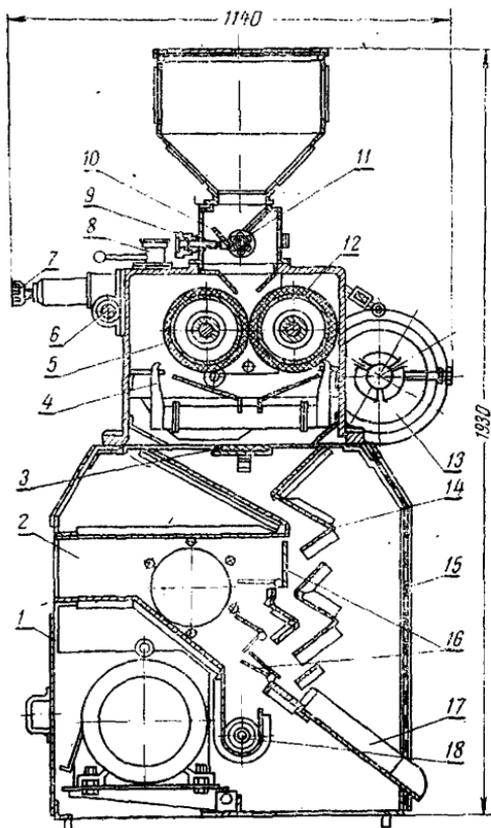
Шелушитель БШР с резиновыми валками, консольный.
